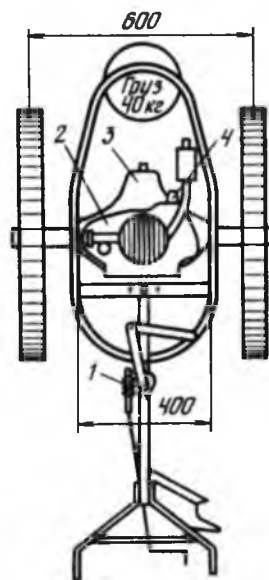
Мотоплуг с двигателем от мотороллера «Тула-200»: 1 — рулевой механизм; 2 — двигатель; 3 — картер косилки; 4 — центробежный регулятор
